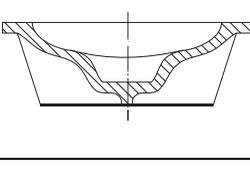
Примеры крепления знаковых частей на моделях отливки
